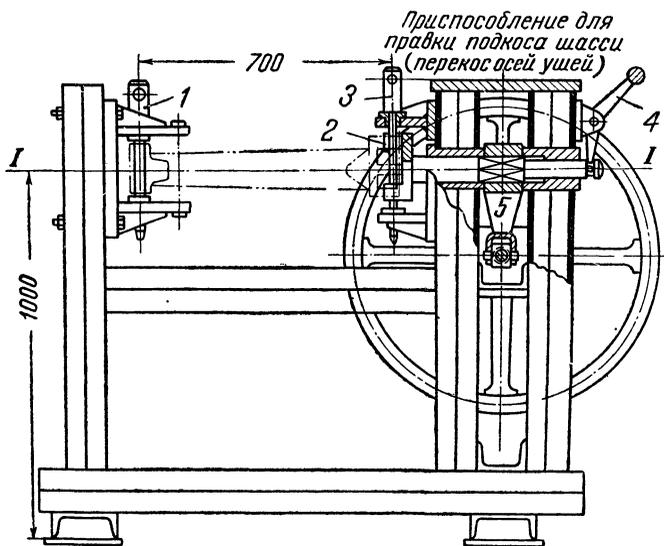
Переносное приспособление для холодной правки элементов сварных узлов и агрегатов.
